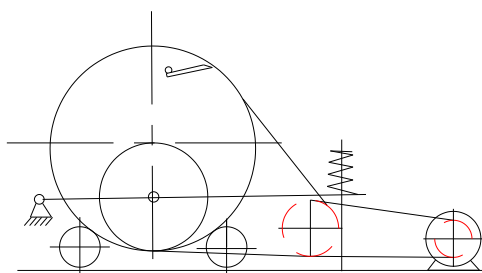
Схеми конструкції барабано-валкового млина безперервної дії
